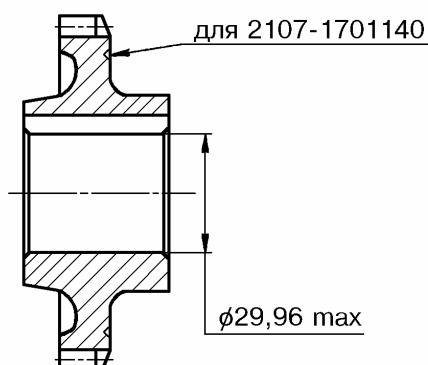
Шестерня заднего хода вторичного вала – 2101-1701140, 2107-1701140.
